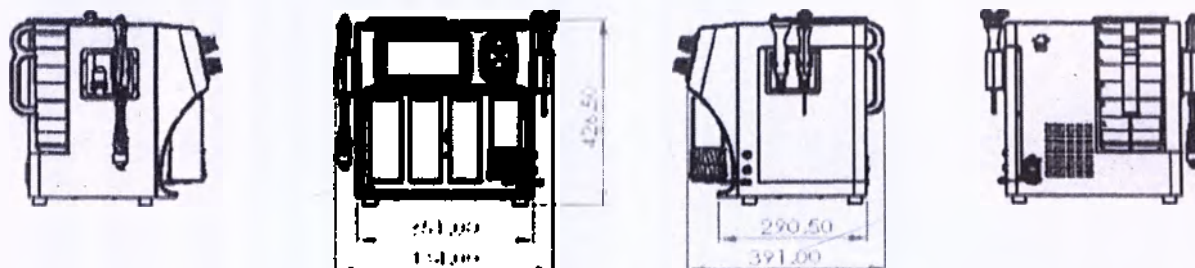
Схематичное изображение и габаритные размеры Основного блока Hydra Touch H2
